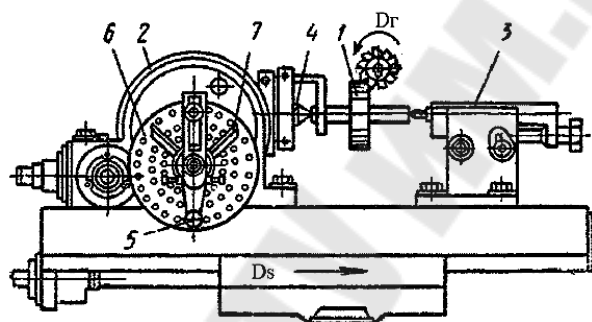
Схема обработки зубчатого колеса в делительной головке
